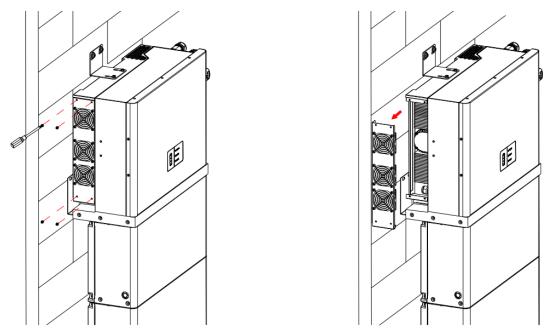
Entfernen der Lüfterbaugruppe
